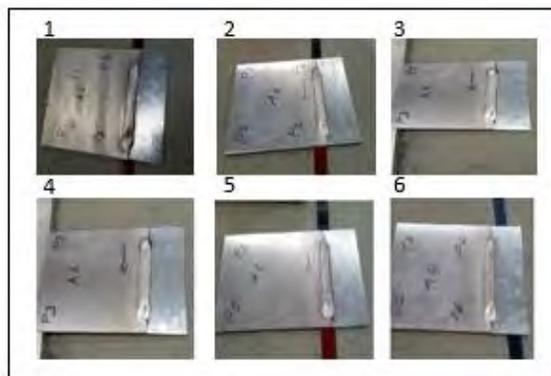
Cordones de soldadura del proceso CMT a un ángulo de 45°
